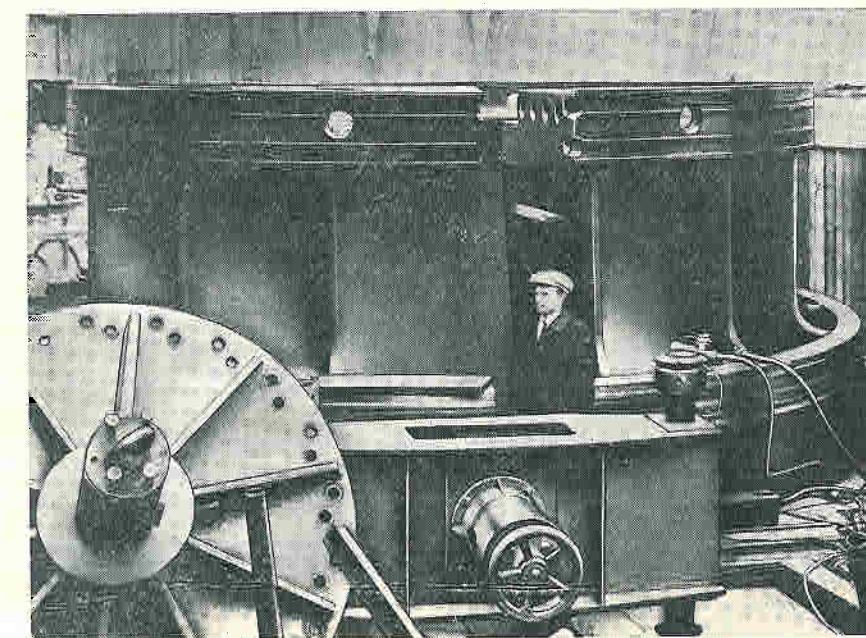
Рабочее колесо гидротурбины Братской ГЭС в процессе подготовки плоскостей разъема под стыковку и сварку половинок
